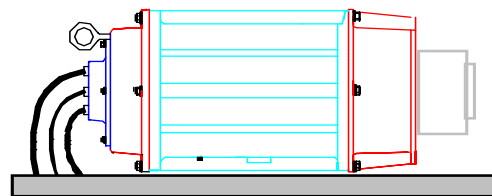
↑ Colocación en posición horizontal de la bomba para desmontaje del impulsor y recambio de los sellos mecánicos.
